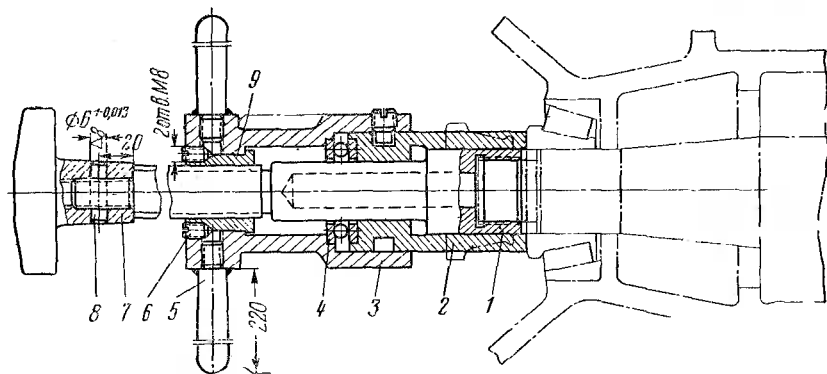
Приспособление для напрессовывания ступицы переднего колеса и подшипников с тормозными барабанами на поворотную цапфу:
